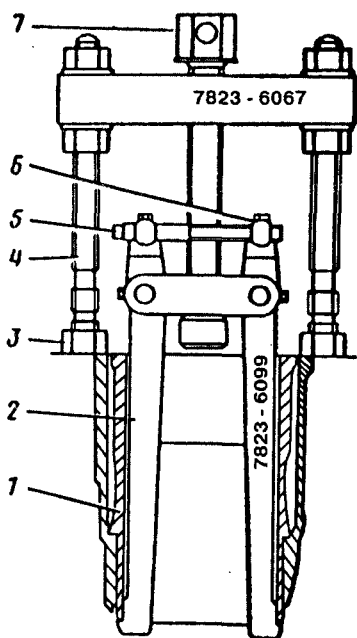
Выпрессовка гильзы из блока цилиндров комбинированным съемником:
